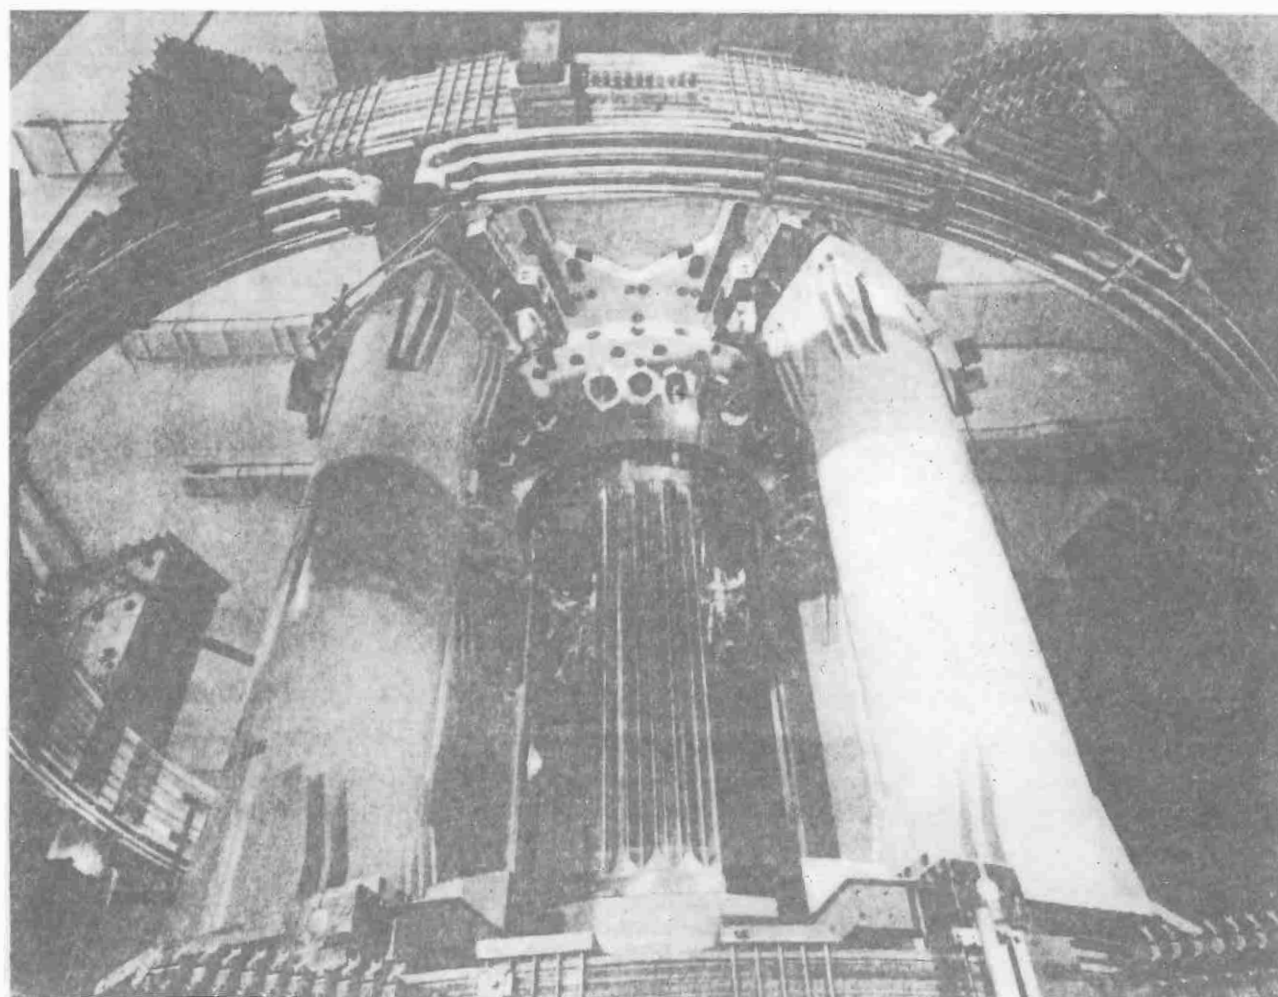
MONTAGGIO DELLE BOBINE DI EQUILIBRIO DEL JET
